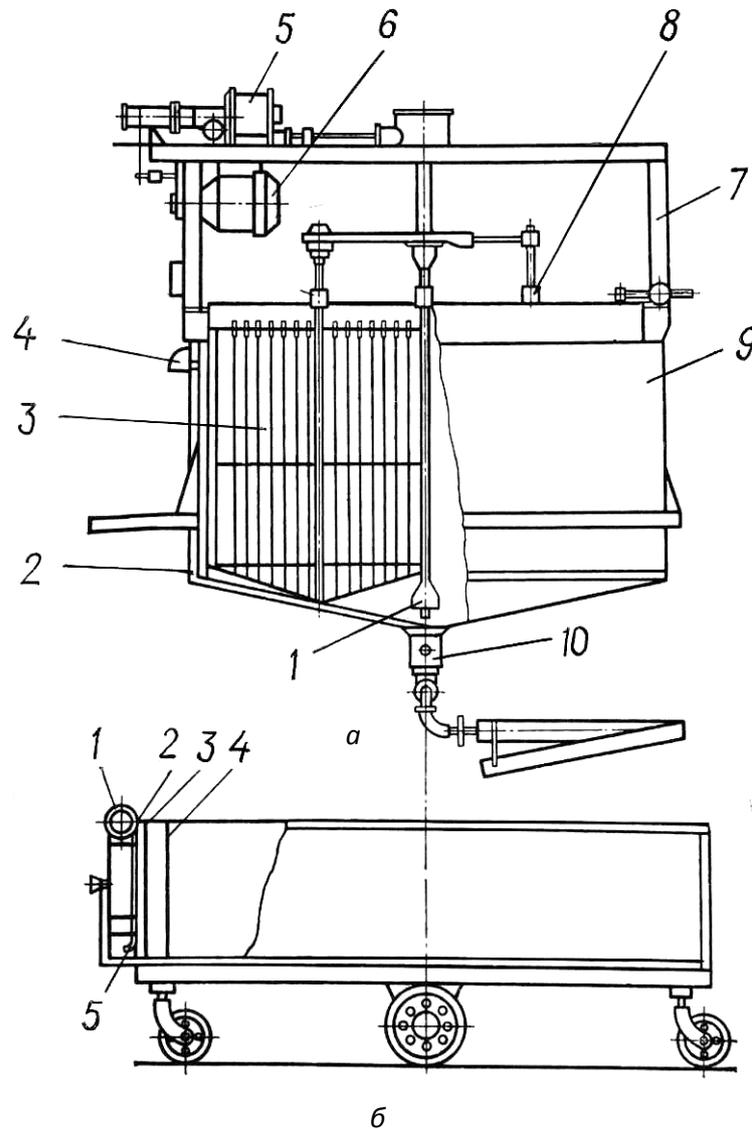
Схема аппарата закрытого типа для выработки сырного зерна: *a* – емкость для выработки сырного зерна: 1 – мешалка; 2 – паровая рубашка; 3 – планетарный нож; 4 – переливной патрубков; 5 – редуктор; 6 – электродвигатель; 7 – стойка; 8 – круговой нож; 9 – кожух; 10 – выпускной кран; *б* – тележка: 1 – патрубков; 2 – кожух; 3 – внутренняя емкость; 4 – щит с отверстиями; 5 – сливная труба
